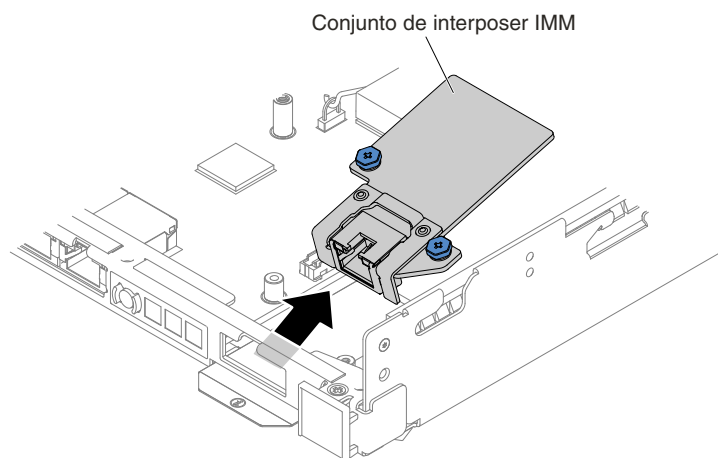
Remoção do conjunto de cabo adaptador de IMM
